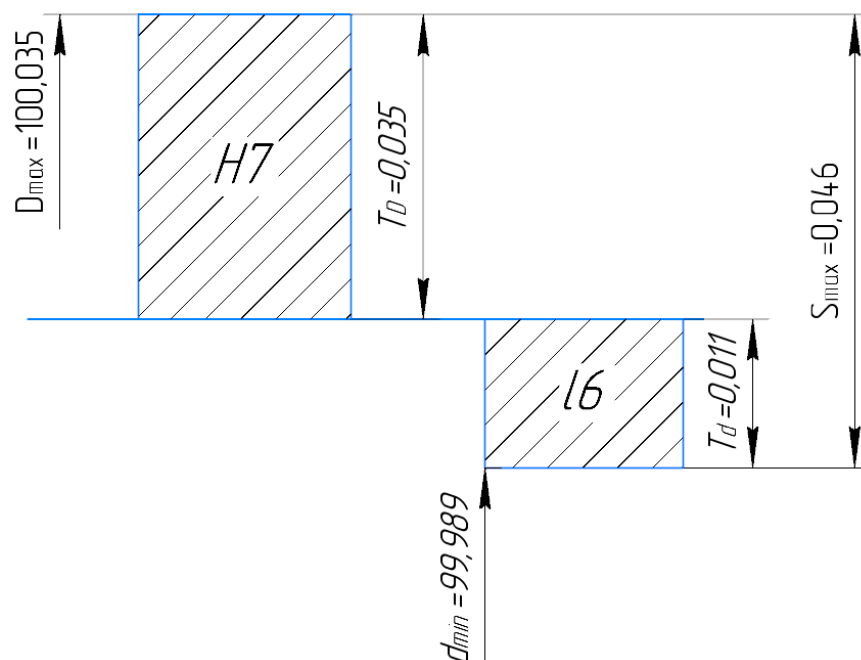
Схема расположения полей допусков для местно нагруженного кольца
